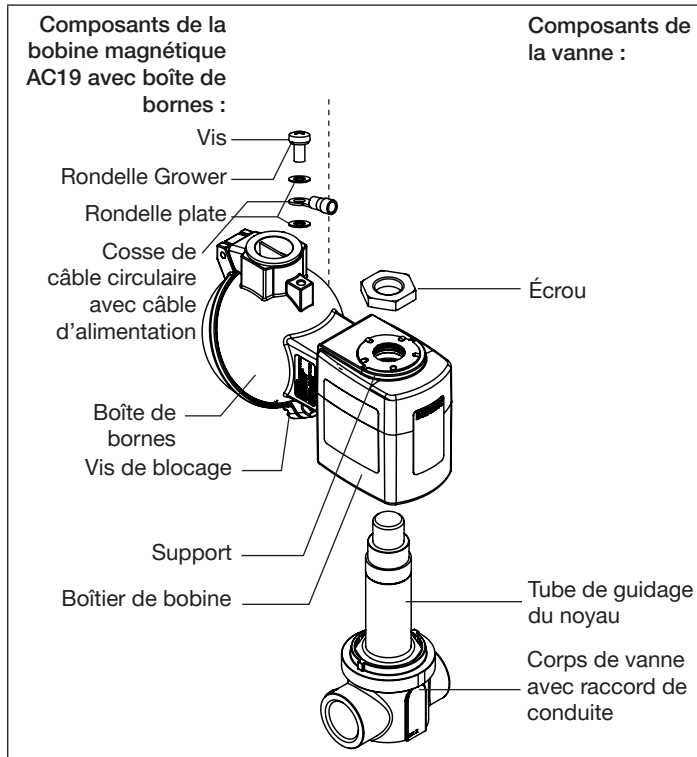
Bobine magnétique type AC19 avec boîte de bornes
